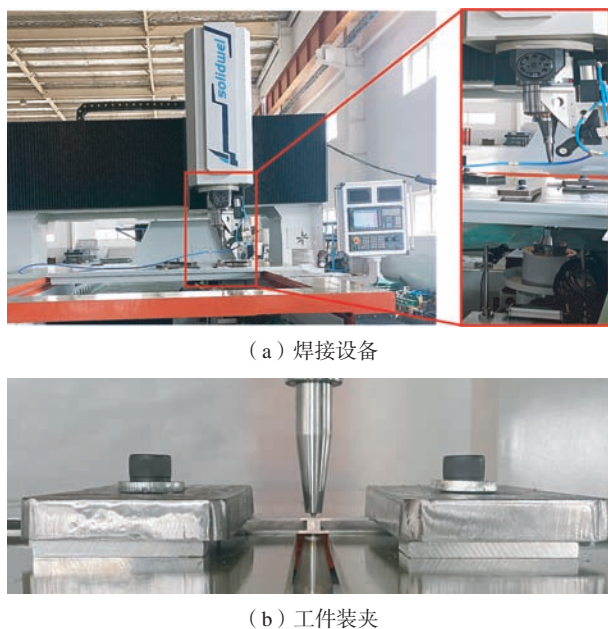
SDS-FSW 焊接设备和工件装夹
